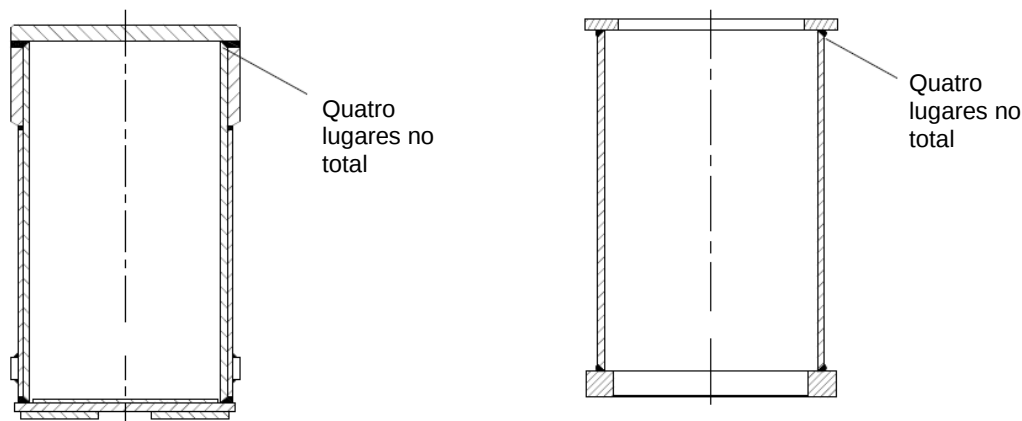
Junções soldadas das vigas corrediças
